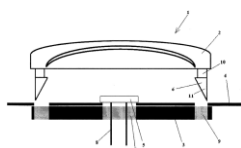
Конструкция крепления светильника для сумки с подсветкой
